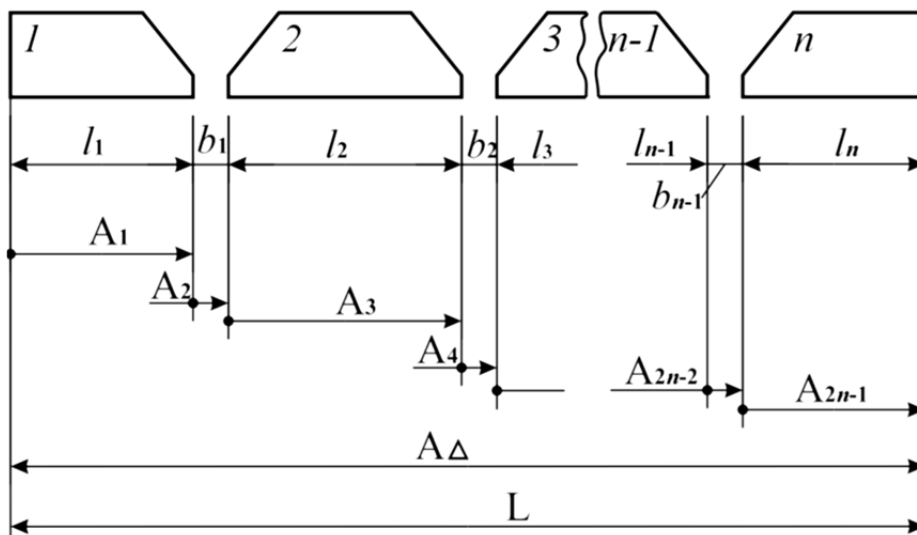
Сборочная размерная цепь из нескольких элементов
